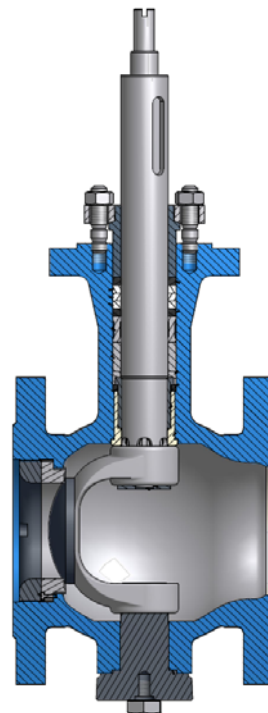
VETEC Drehkegelventil - Schnittzeichnung
